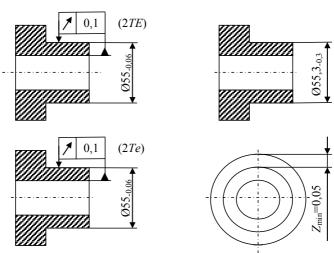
a — эскиз детали; δ — эскиз заготовки; ϵ — эскиз механической обработки; ϵ — схема снятия равномерного припуска
